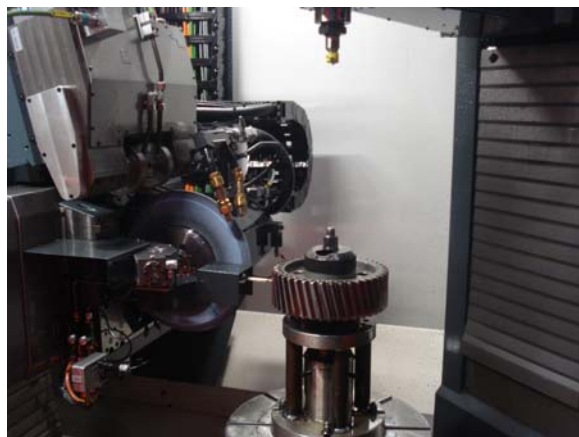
Обработка зубчатого колеса на зубошлифовальном станке мод. HOFLEER RAPID 1250.
